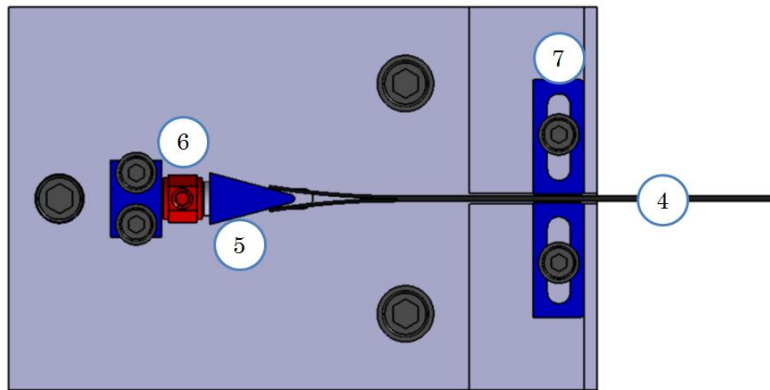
Montage de délaminage dynamique (épreuve et coin)
